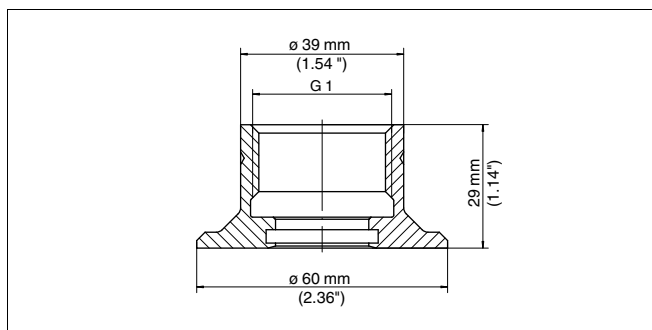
Medidas da luva soldada G1 A conforme DIN 3852-X
